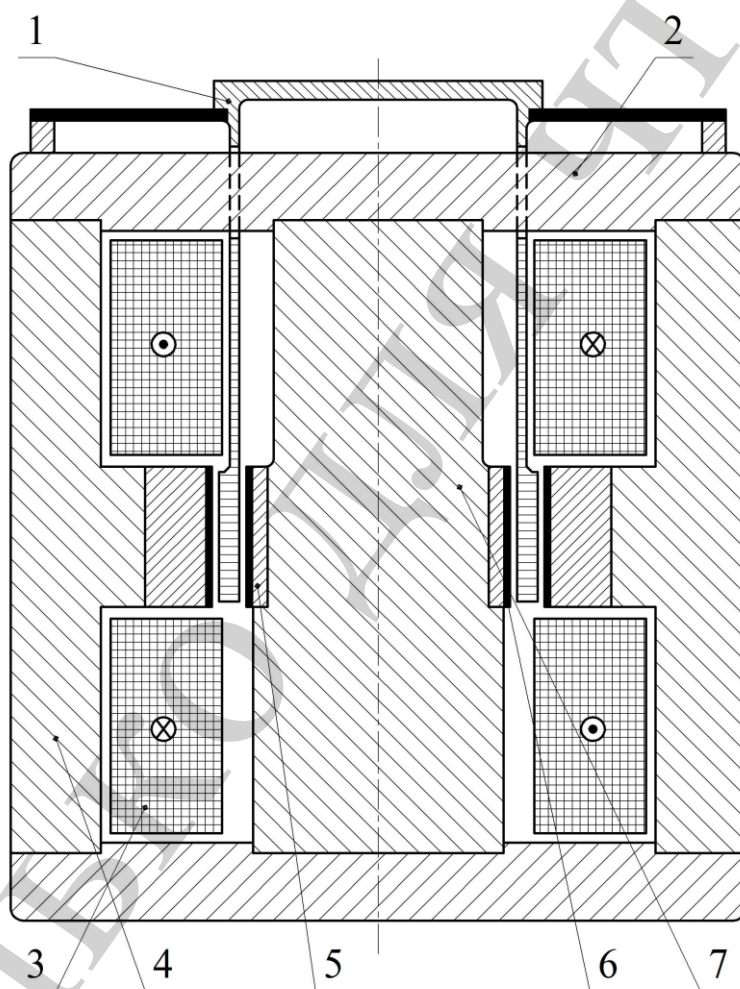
Схема электродинамического линейного двигателя возвратно-поступательного движения: 1 – подвижная катушка; 2 – фланец магнитопровода; 3 – катушка подмагничивания; 4 – корпус магнитопровода; 5 – катушка управления; 6 – экран; 7 – стержень
